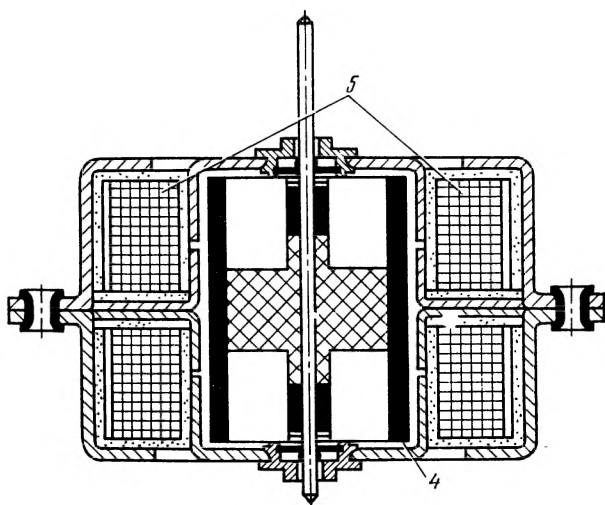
Схематическое устройство двигателя ТСК-1: 4 — ротор; 5 — статорные обмотки
